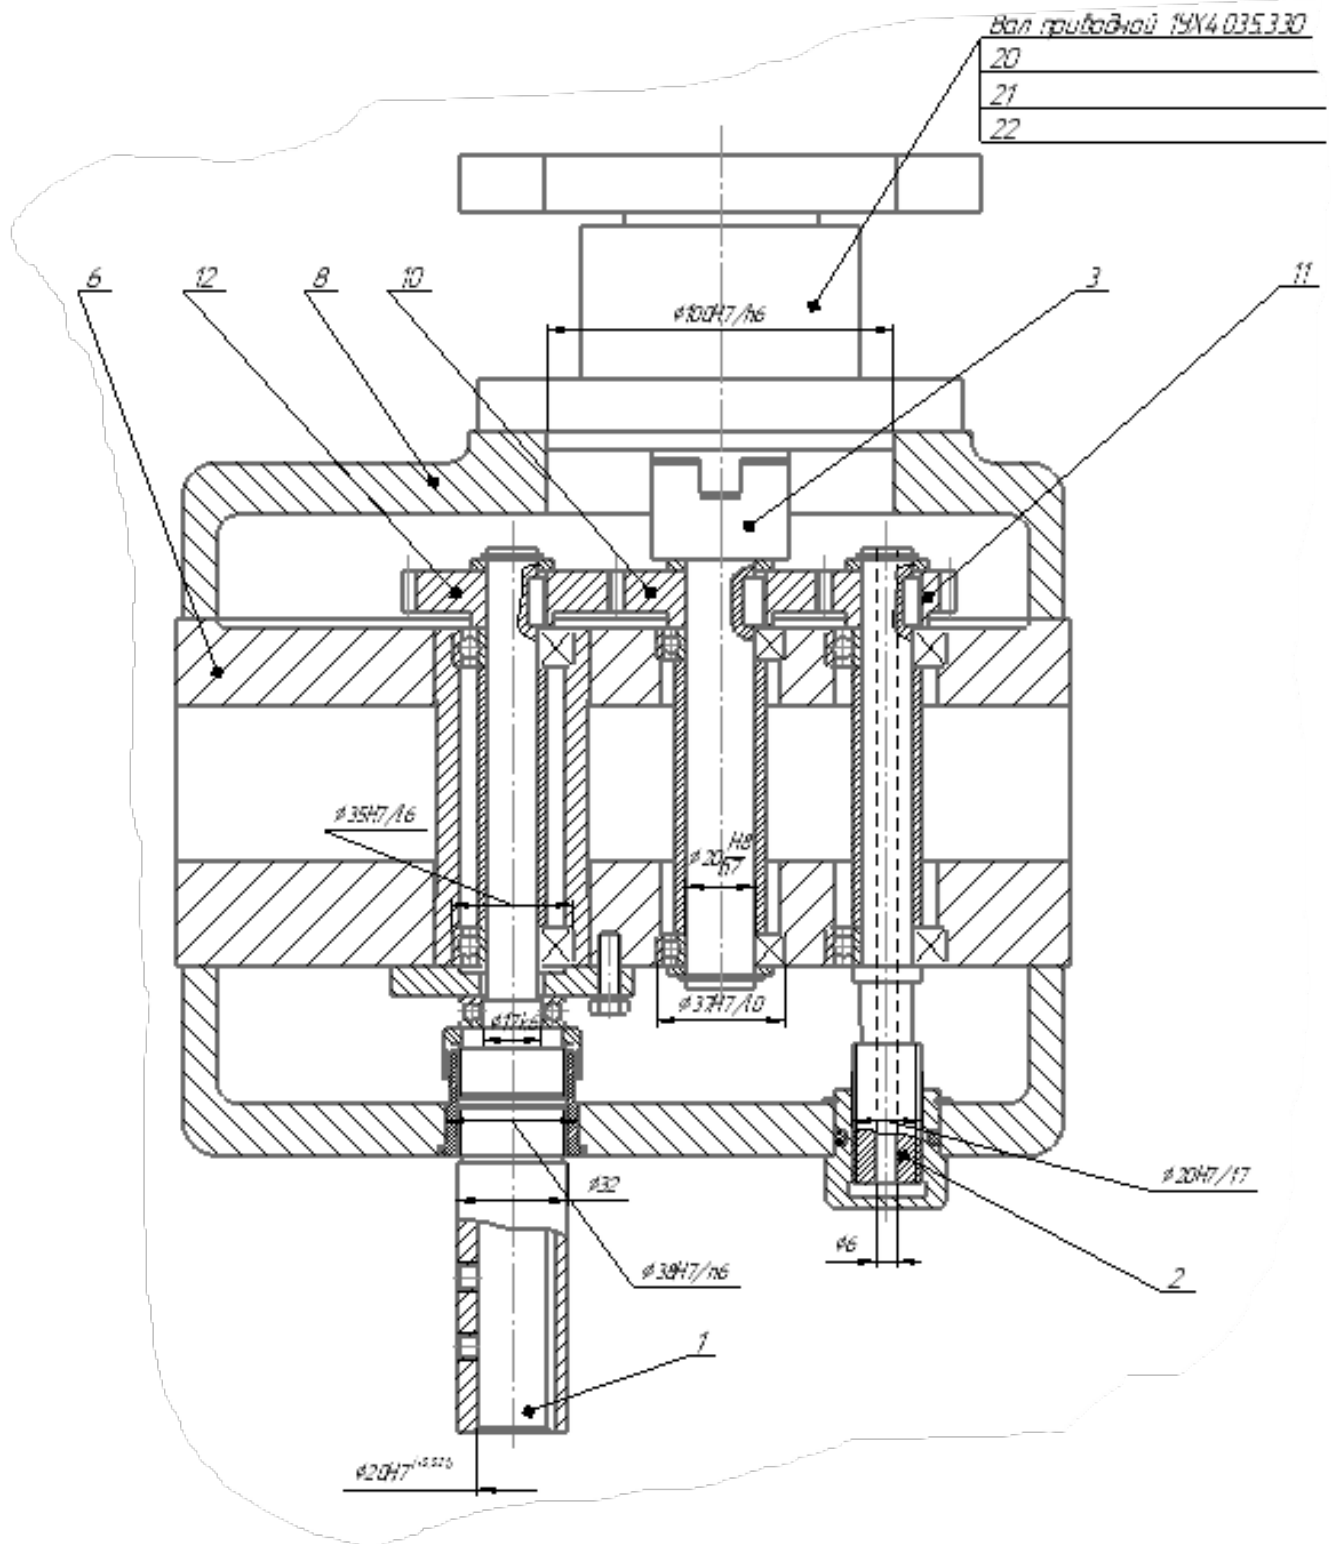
Принципова схема багатошпindelної насадки
